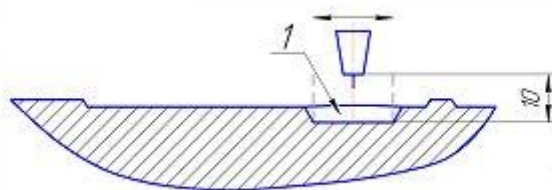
Схема підготовки зварювального пальника до накладення першого валика
